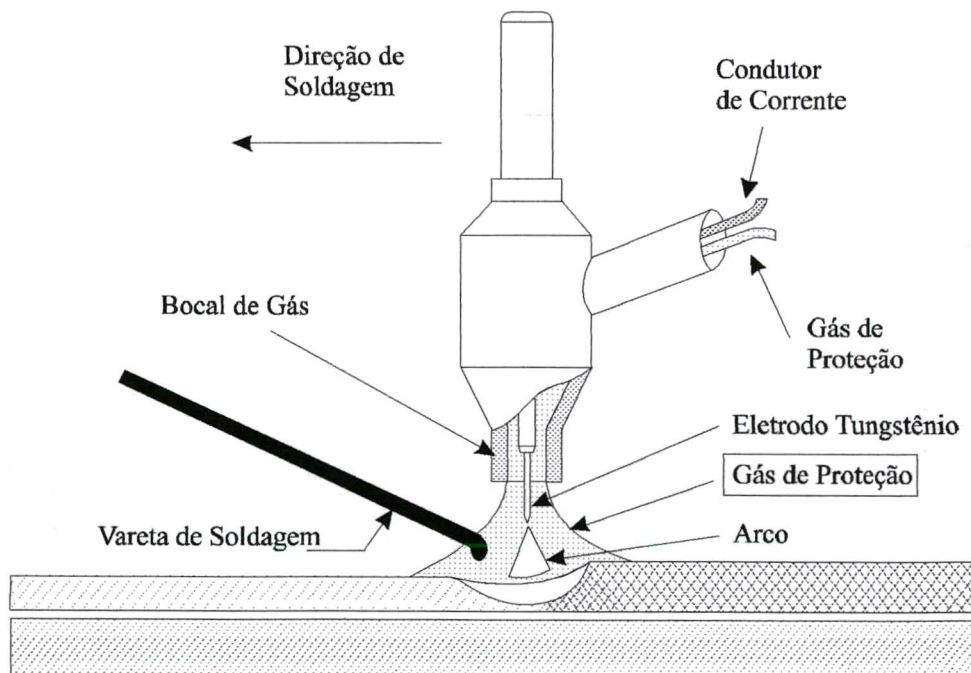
Processo de soldagem TIG – Tungsten Inert Gas
